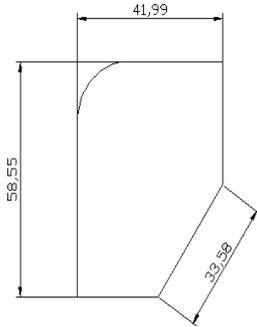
Горизонтальный, вертикальный и параллельный размеры
